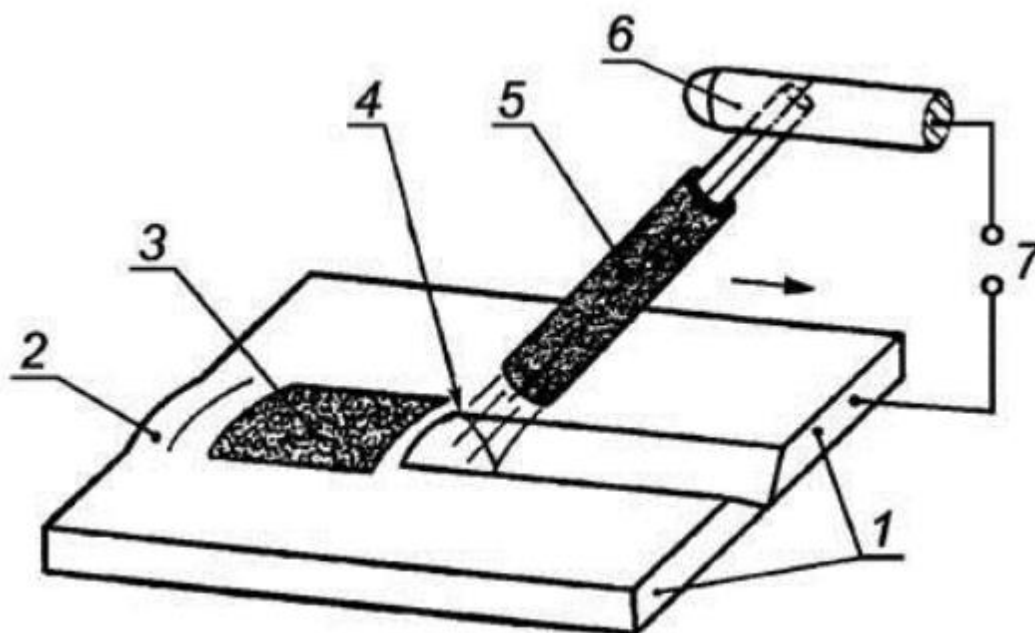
Схема ручной дуговой сварки покрытыми электродами
